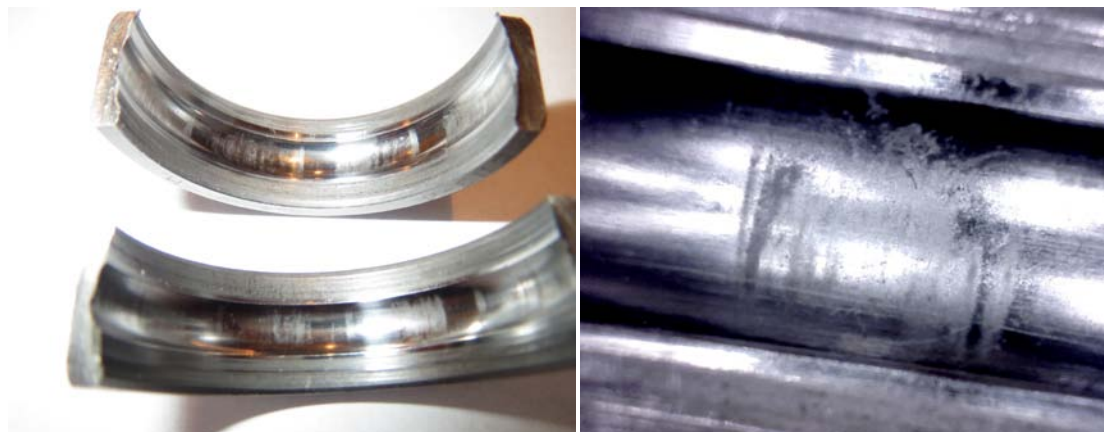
Фотография начала усталостного разрушения дорожки внешнего кольца подшипника
